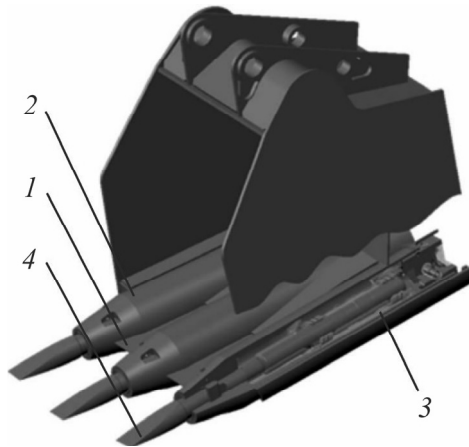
Конструкция ковша активного действия экскаватора: 1 — передняя стенка ковша; 2 — кожух гидроударного устройства (ГУ); 3 — гидроударное устройство; 4 — ударный зуб
